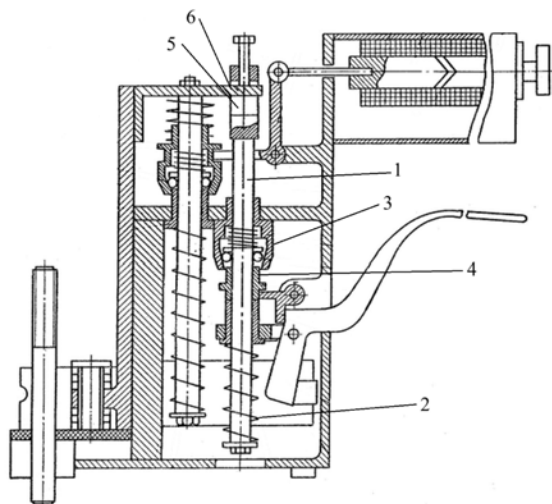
Пістолет із механізмом керування глибиною занурення шпильки в зварювальну ванну
